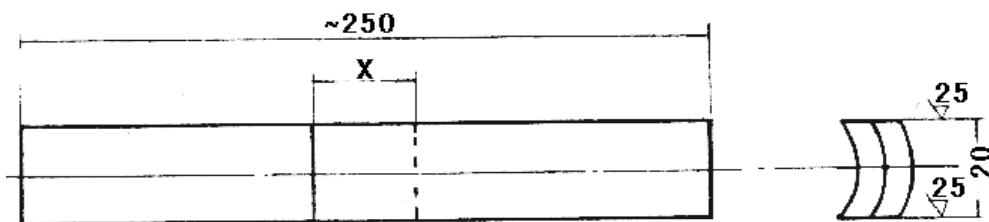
直径 > 76mm 管状钎焊接头拉伸试样
